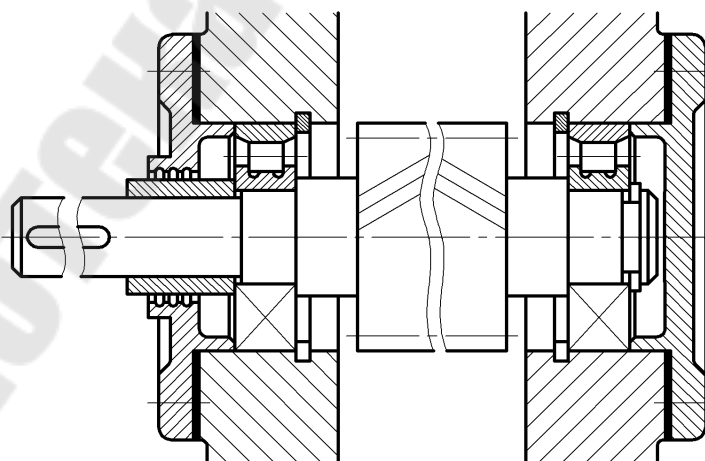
Подшипниковый узел «плавающий» на роликоподшипниках с наружными кольцами без бортов
